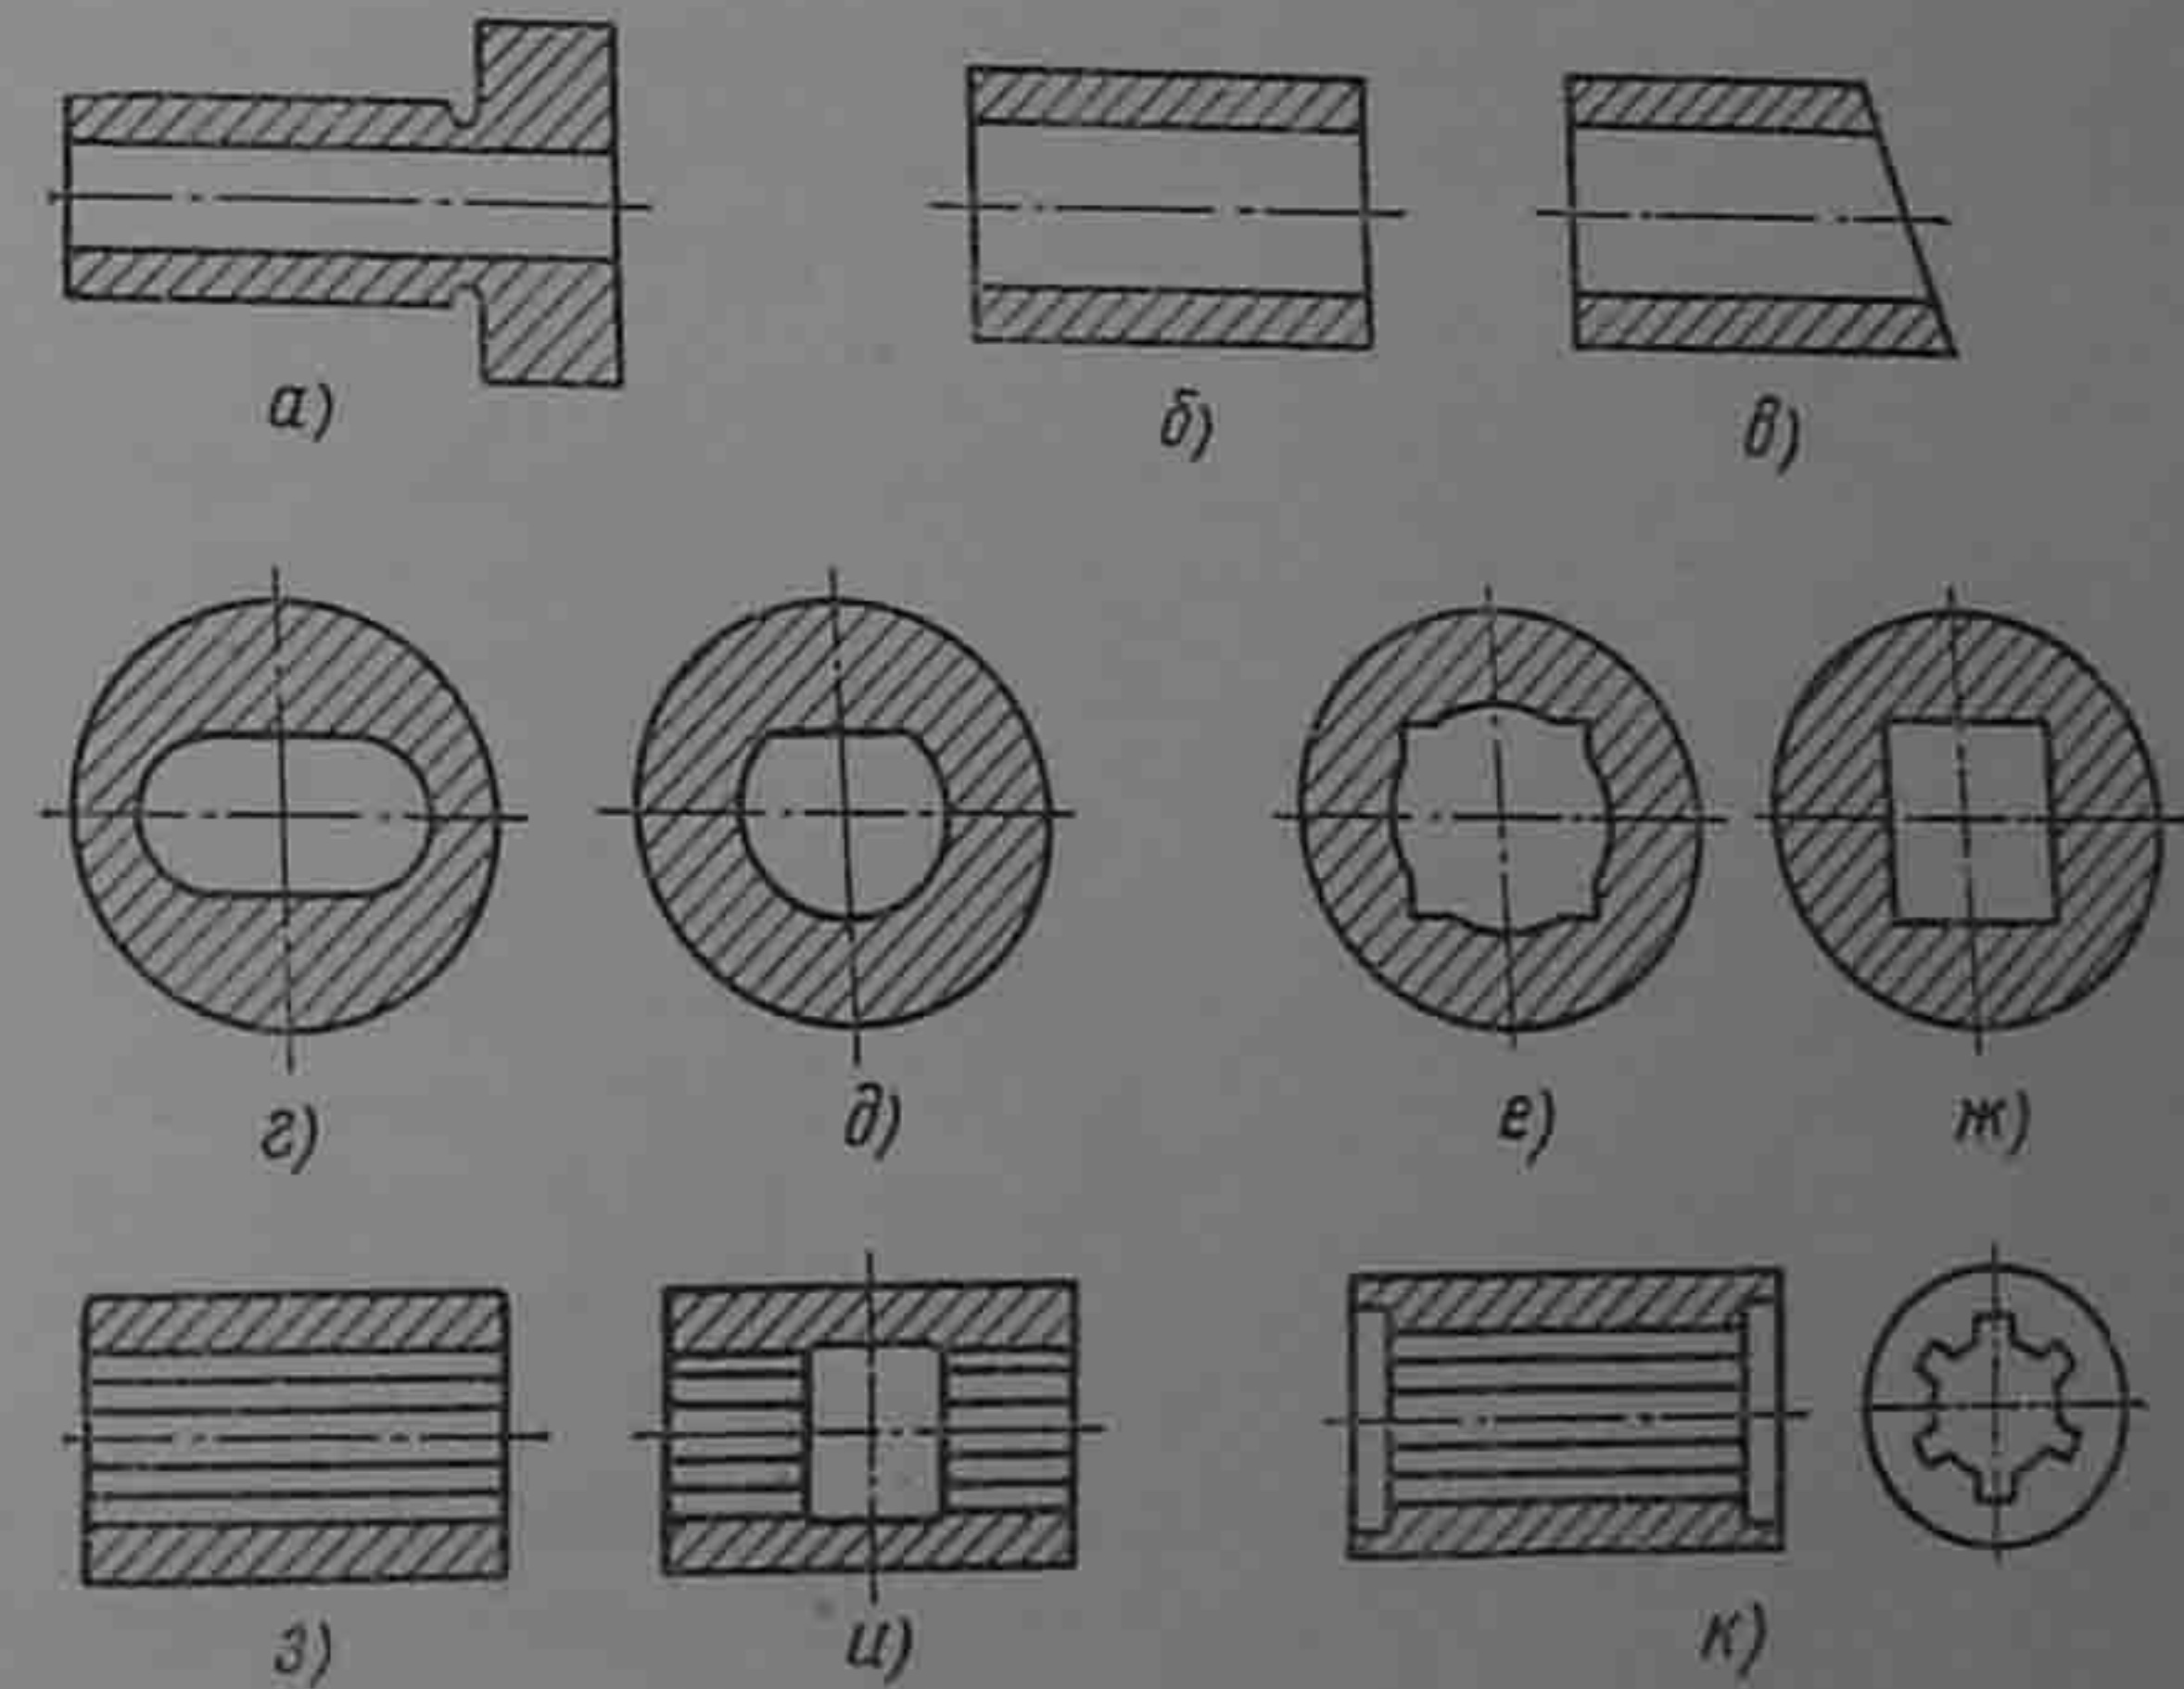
Примеры конструкций деталей машин, обрабатываемых на протяжных станках
